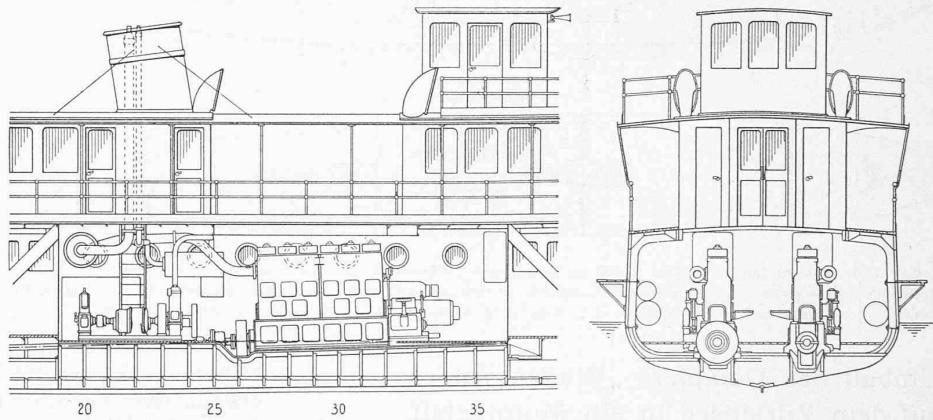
(darunter). Maschinenraum, Längs- und Querschnitt 1:140.
